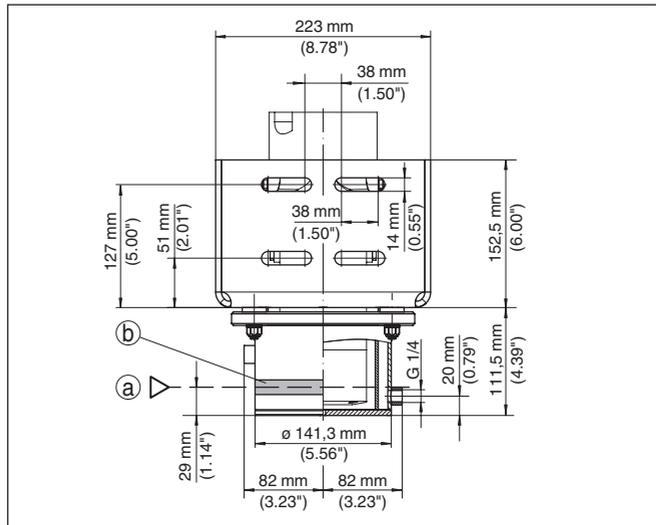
Position der Sensormarkierung und Bohrloch des Befestigungswinkels - POINTRAC 31, kurze Ausführung (45 mm)
